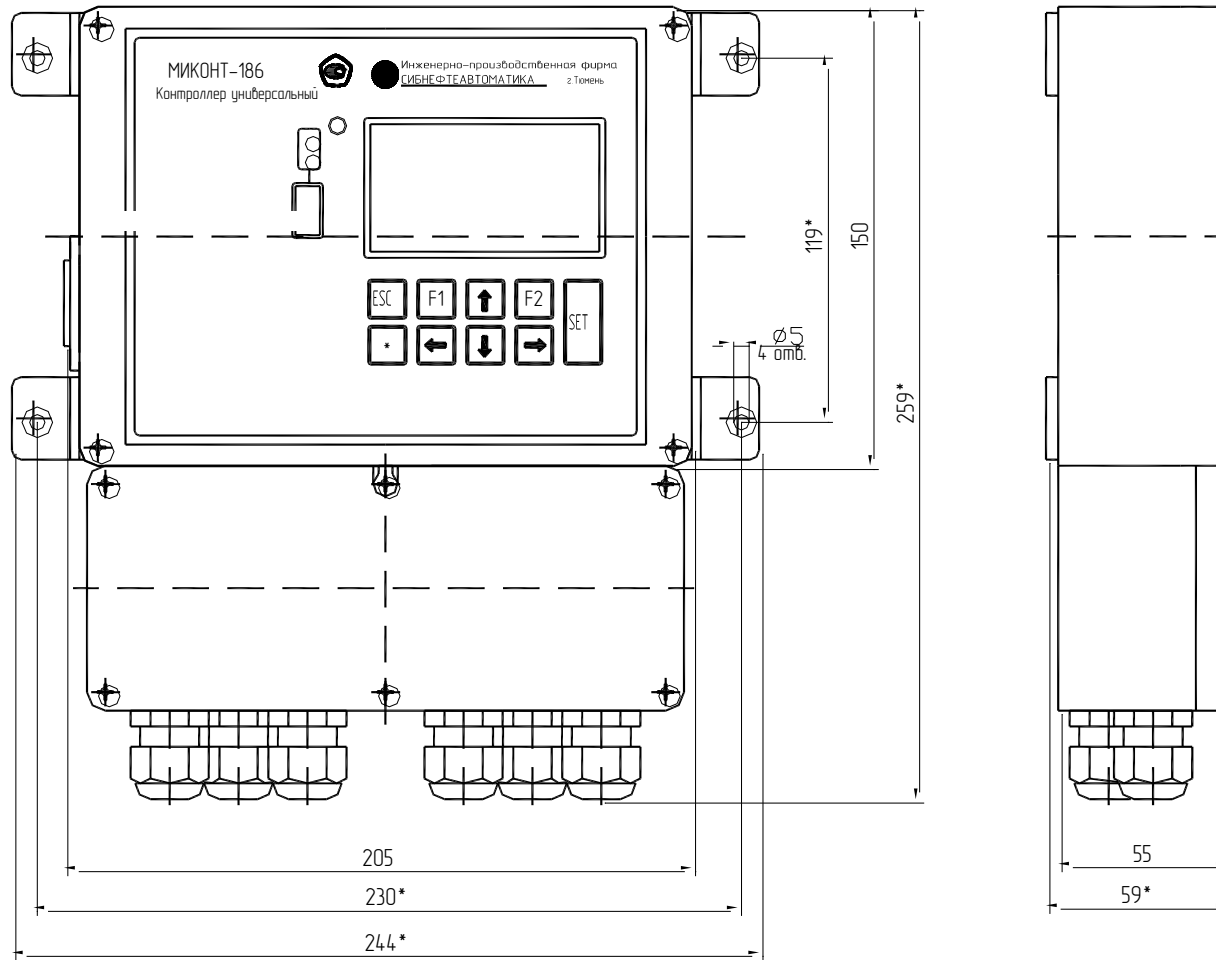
Контроллер универсальный МИКОНТ-186
